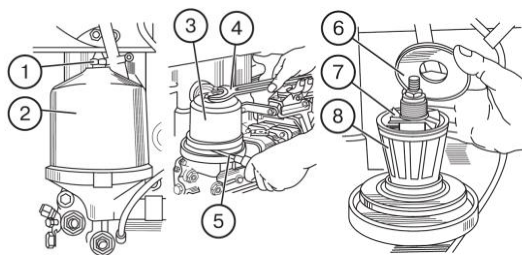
Схема разборки масляных фильтров двигателя и коробки передач
